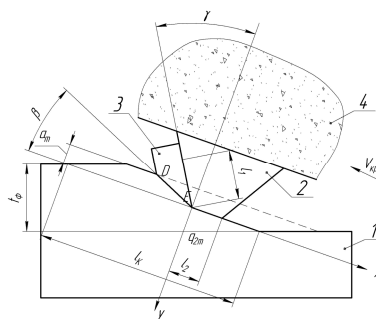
Схема контакта режущего АЗ с заготовкой:
